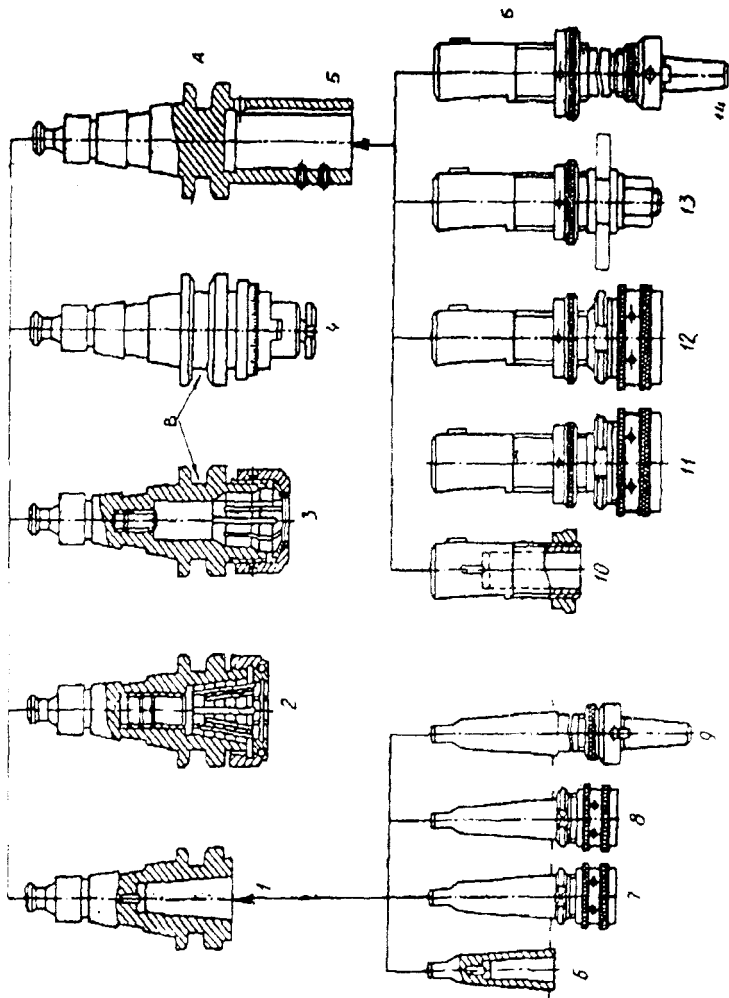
Система вспомогательного инструмента к станкам с ЧПУ
